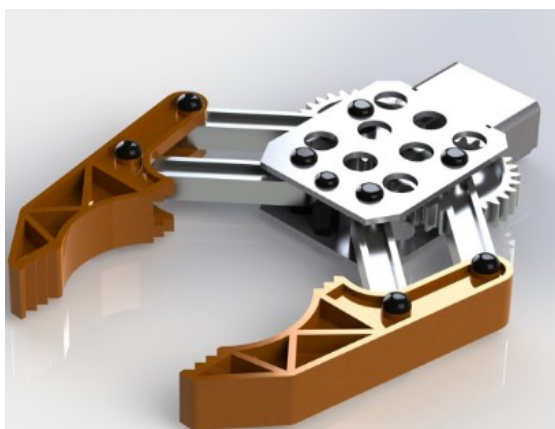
ПР ЗУ схватывающего типа, сменяемый
